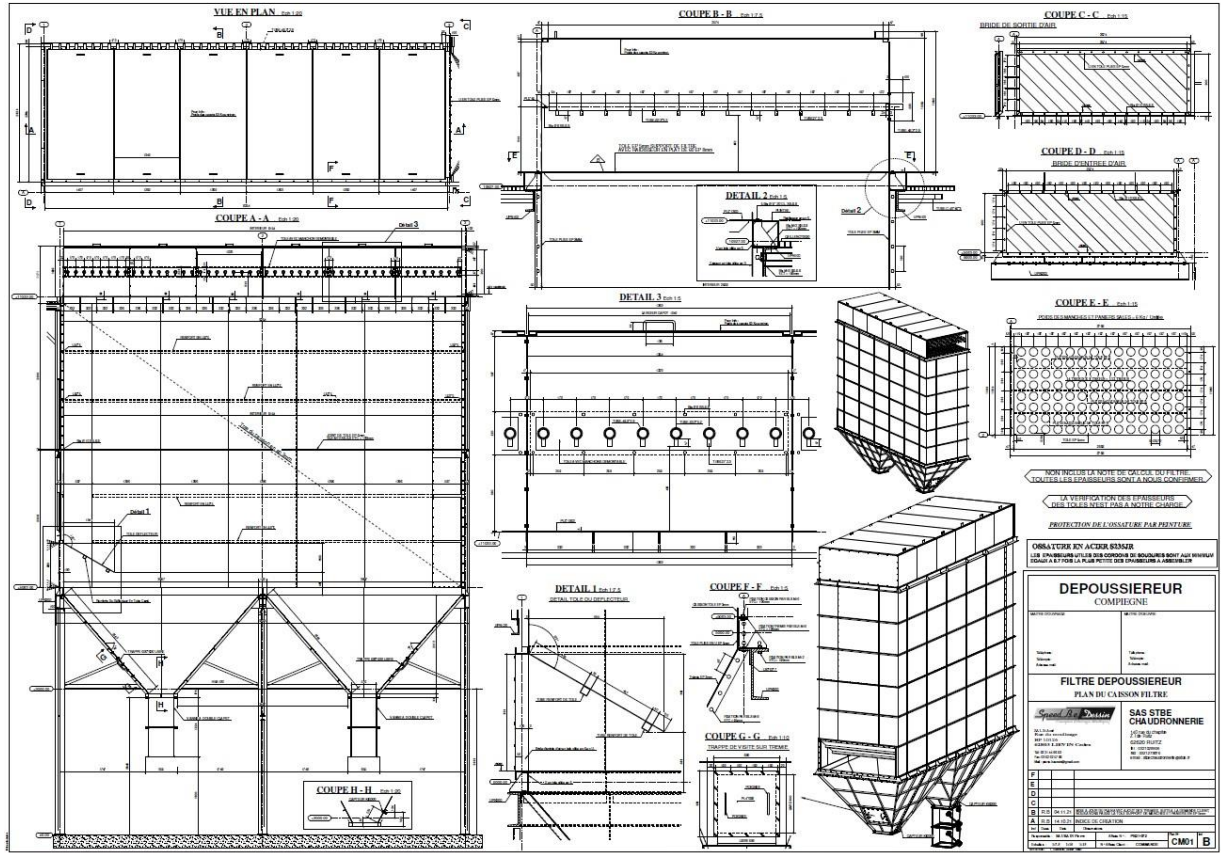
PLAN D'UN FILTRE DÉPOUSSIÉREUR
